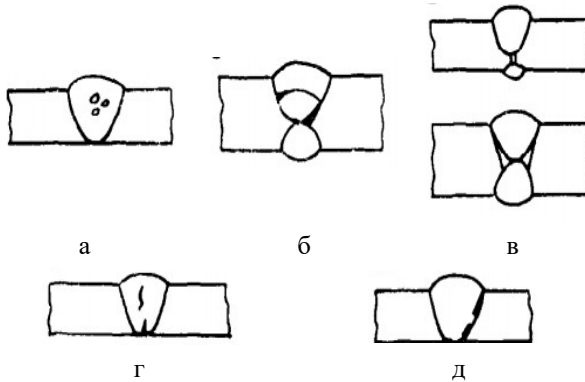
Внутрішні дефекти зварних швів: а – пори; б – шлакові включення; в – непровари в корені шва і по кромці; г – тріщина; д – несплавлення
